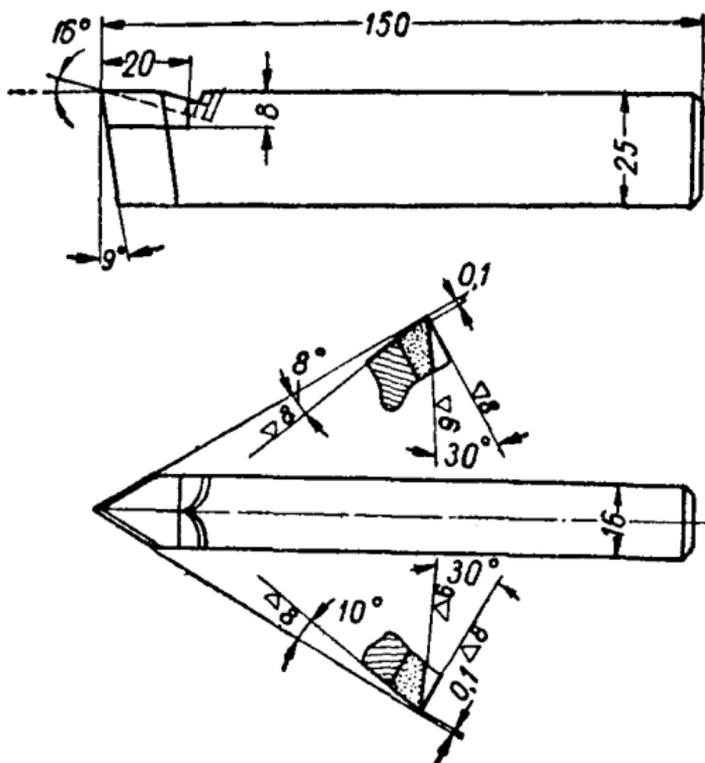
Резьбовой резец для нарезания резьбы на деталях из жаропрочных сталей.
